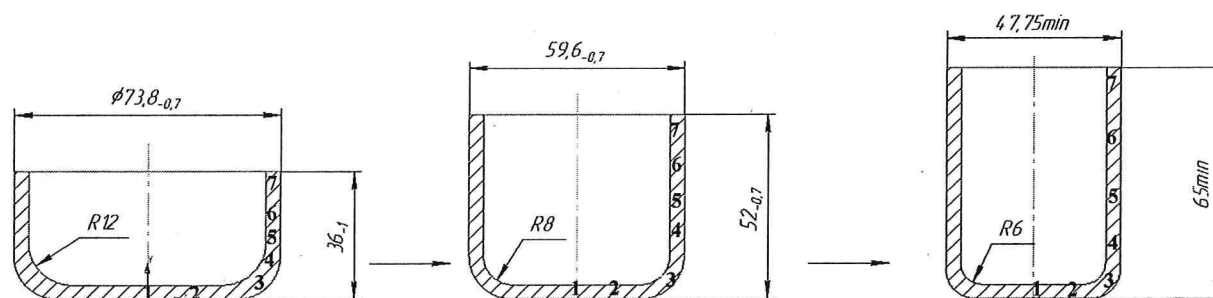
Основные размеры и контрольные точки в заготовках стакана по переходам.
